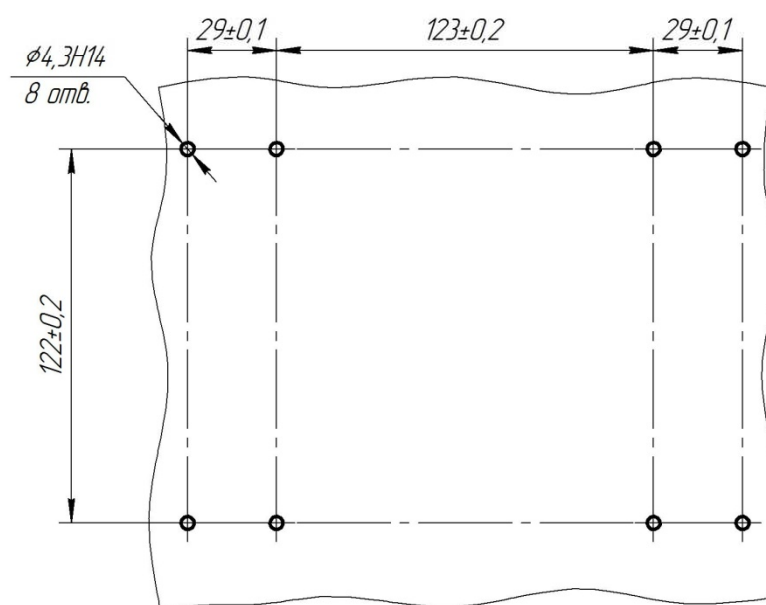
Габаритные и присоединительные размеры устройства при внешнем монтаже, обеспечивающем поворот вниз (вверх)
